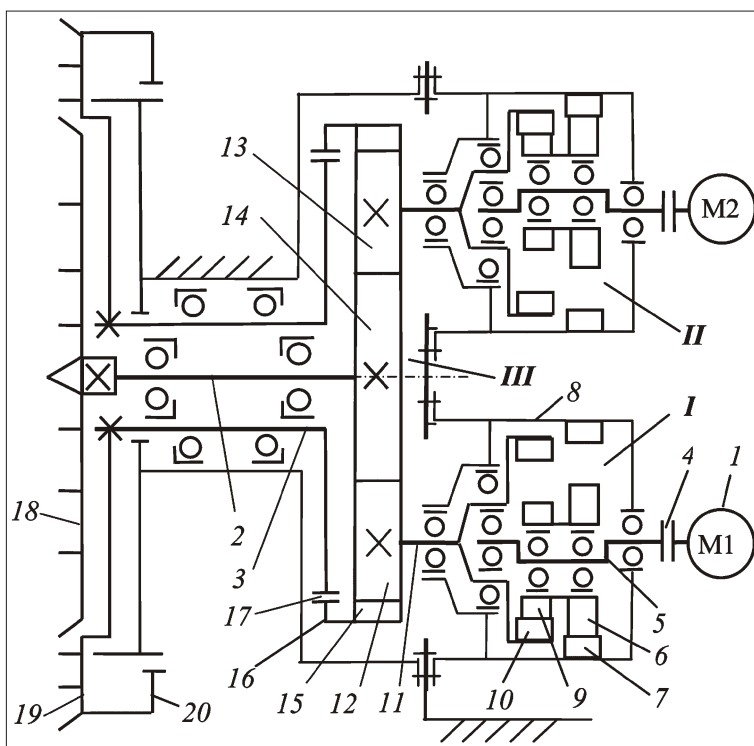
Кинематическая схема привода соосных роторов со спаренными планетарными редукторами с ведущими водилами (вариант 5)
